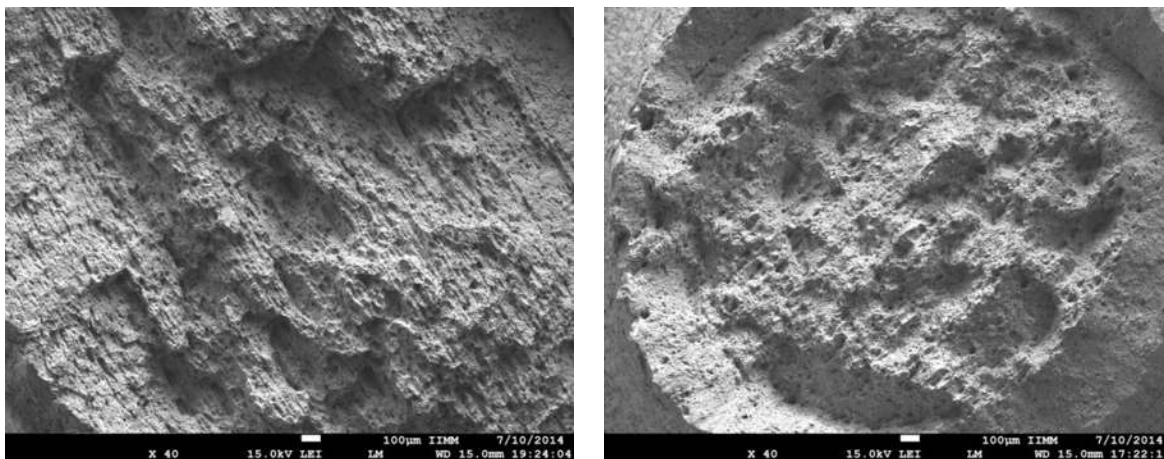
26.- Fractografía de la soldadura 8-1(Unión simple, condición 2).
